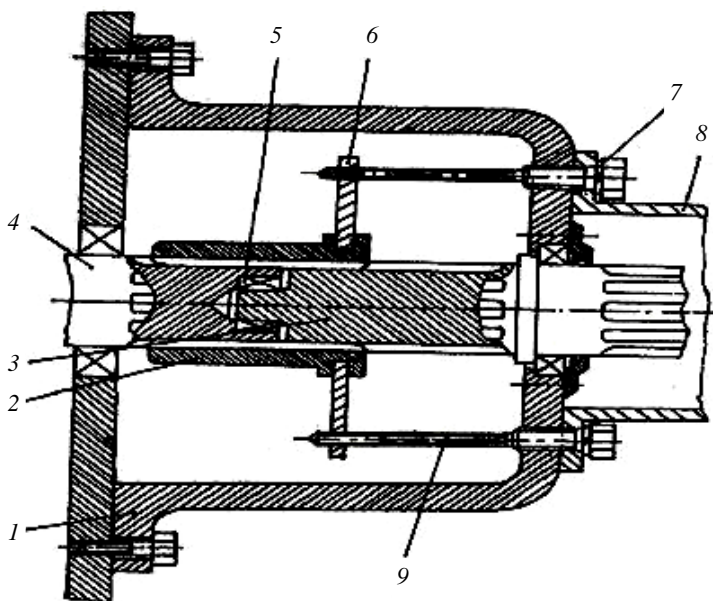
Схема предохранительного устройства для карданного вала:
